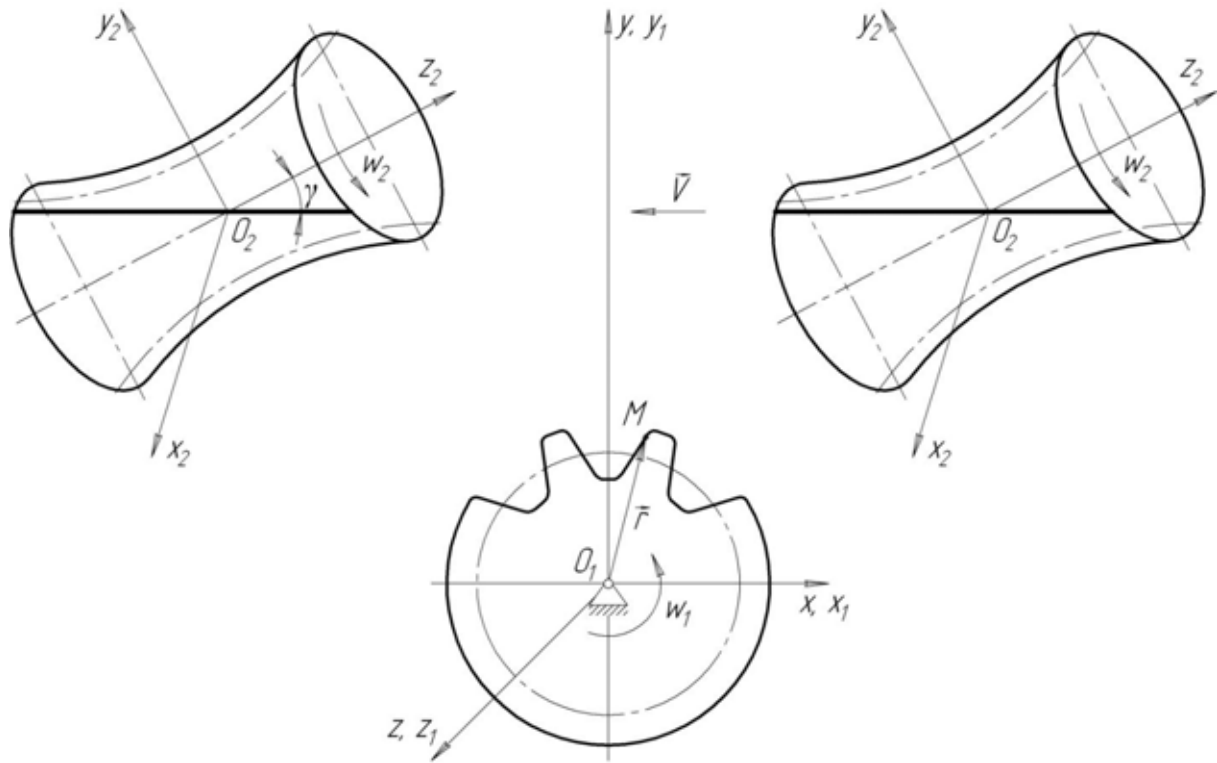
Схема формообразования гиперboloидного зубчатого колеса
